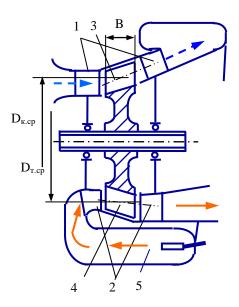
Схема применения турбокомпрессора с общим рабочим колесом в качестве простого ГТД с прямоточной схемой движения потоков: 1 — компрессорная часть; 2 — турбинная часть; 3 — компрессорный рабочий канал; 4 — турбинный рабочий канал; 5 — камера сгорания
